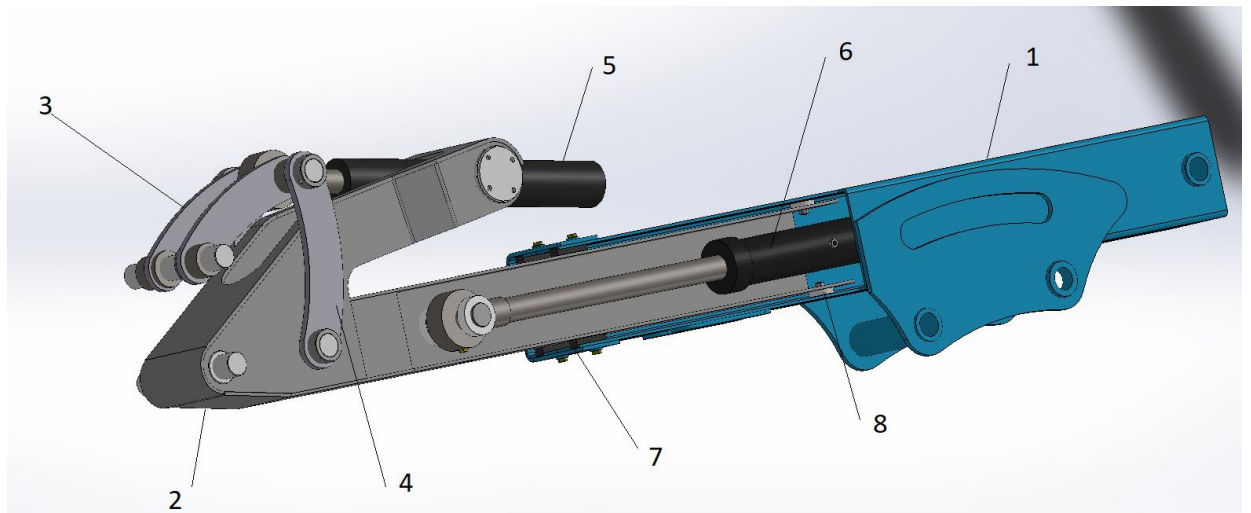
Vista en detalle del mecanismo del brazo telescópico
